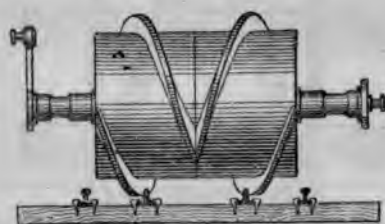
Vue du pignon à dents hélicoïdales engrenant avec la crémaillère Wetli.
